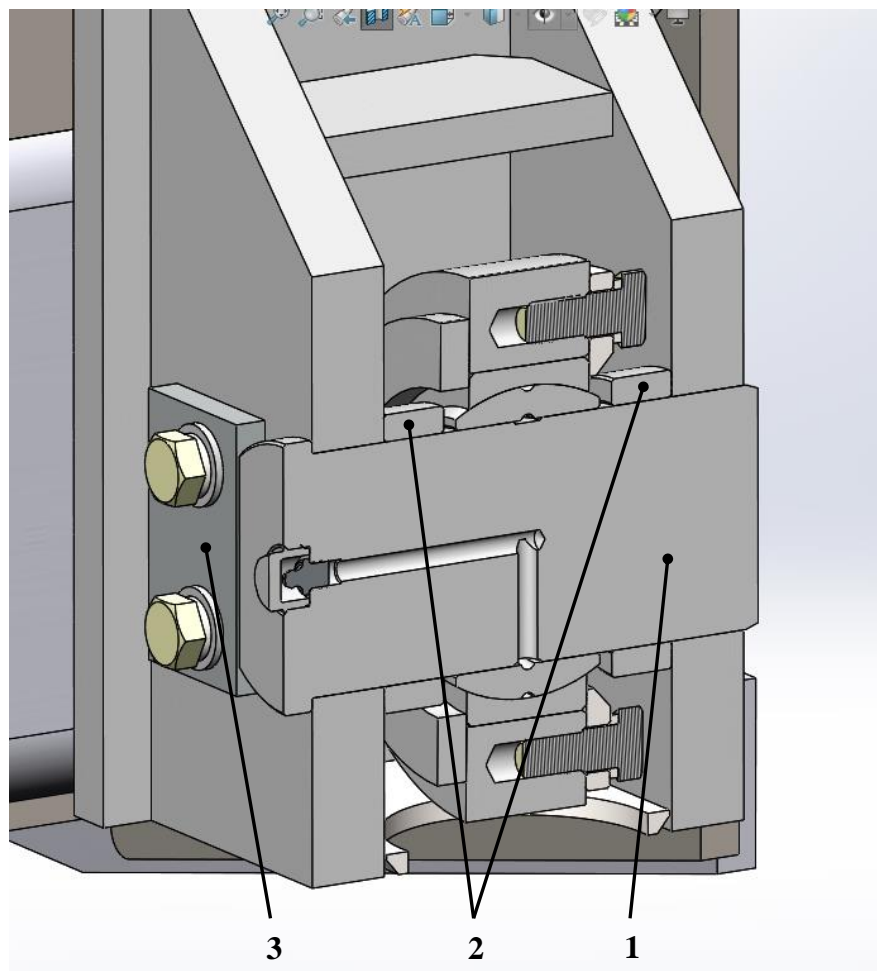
Установка пальца крепления зеркала отвала к брусу
